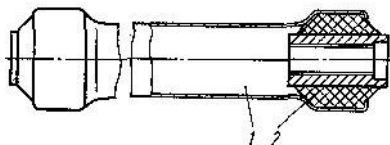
Карданный вал мод. 343/360 фирмы «Вольво». На этих автомобилях автоматическая коробка передач, называемая «Вариоматик», размещена сзади и образует единый блок с главной передачей (см. рис. 3.9). Труба карданного вала выполнена из алюминиевого сплава $AlMgSi\ 0,5F22$ с $\sigma_{B215}\text{ МПа}$, $\sigma_{0,2}\geq 160\text{ МПа}$, $\delta_s\geq 12\%$:
